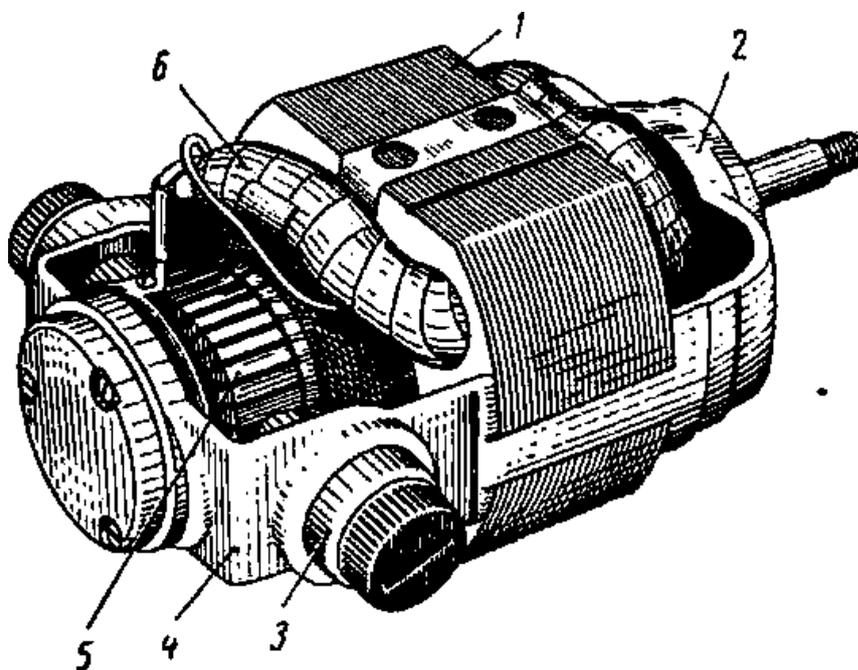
Универсальный коллекторный электродвигатель серии УВ: 1 - статор; 2 - подшипниковый щит; 3 - обойма щеткодержателя; 4 - скоба с гнездом для подшипника; 5 - якорь; 6 - обмотка возбуждения
